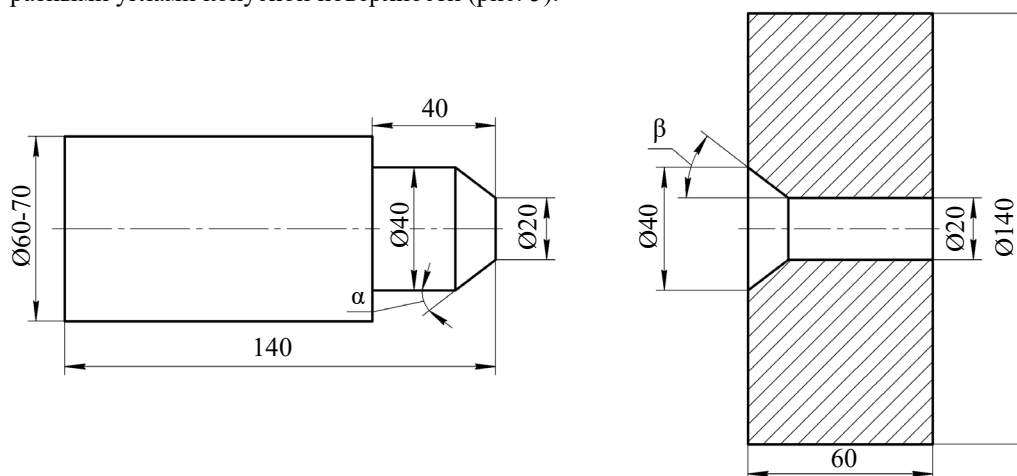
Модель штуцерного узла: α — угол конуса штуцера; β — угол конуса корпуса
